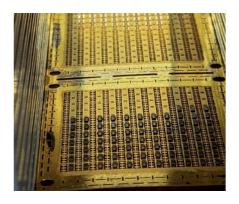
Разваренные ИС в металлополимерном корпусе DFN-6
